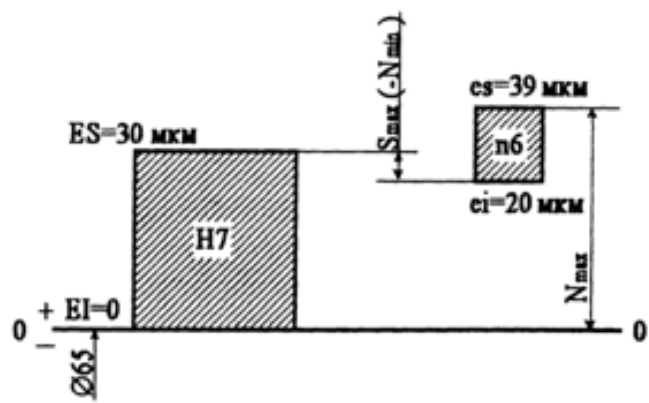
Схема розташування полів допусків посадки 65 H7/n6
